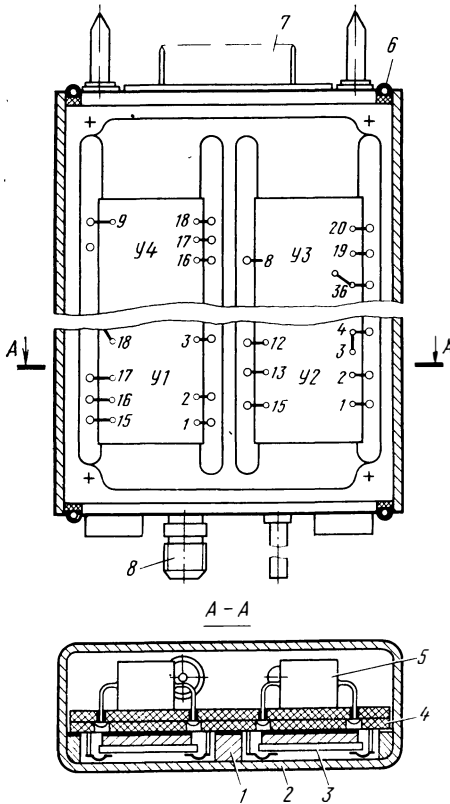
Пример компоновки усилителя с бескорпусными гибридными ИМ
